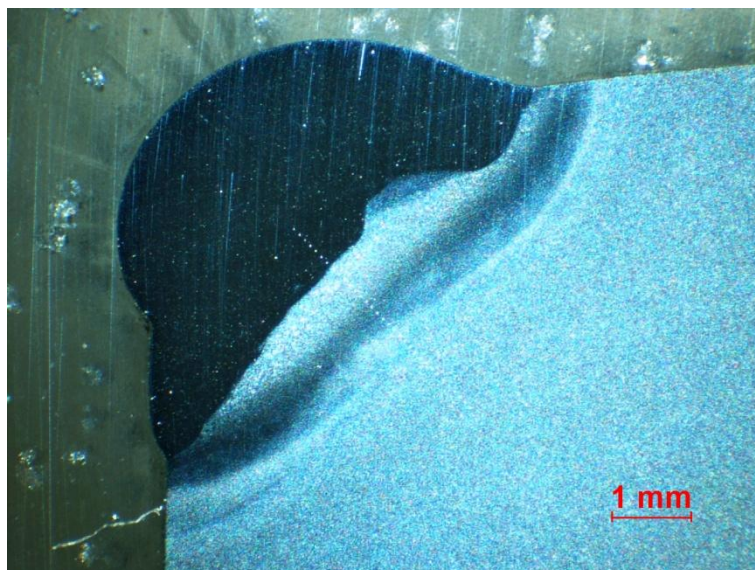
Makrostruktura návaru u vzorku č. 1
